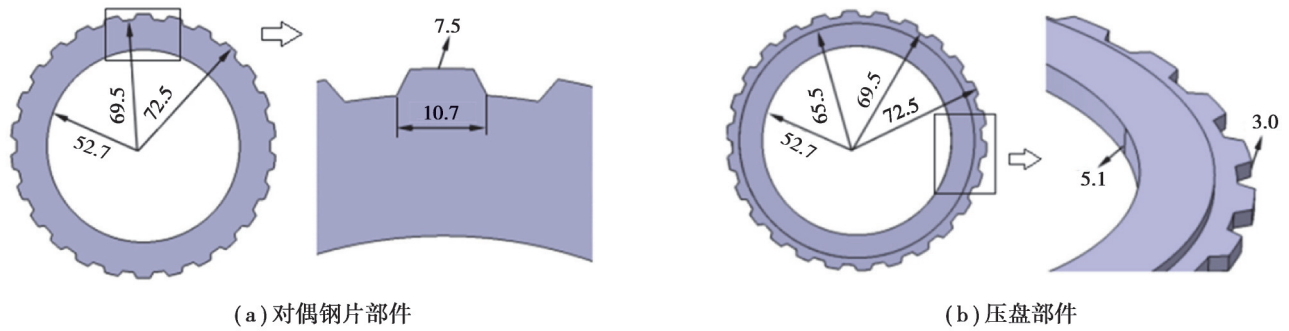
离合器部件模型及局部视图尺寸(单位:mm)
